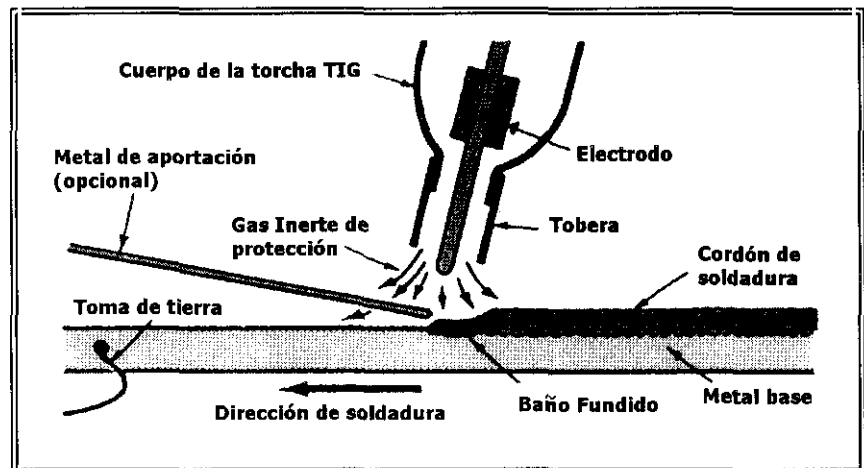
Esquema del proceso de soldadura TIG.
